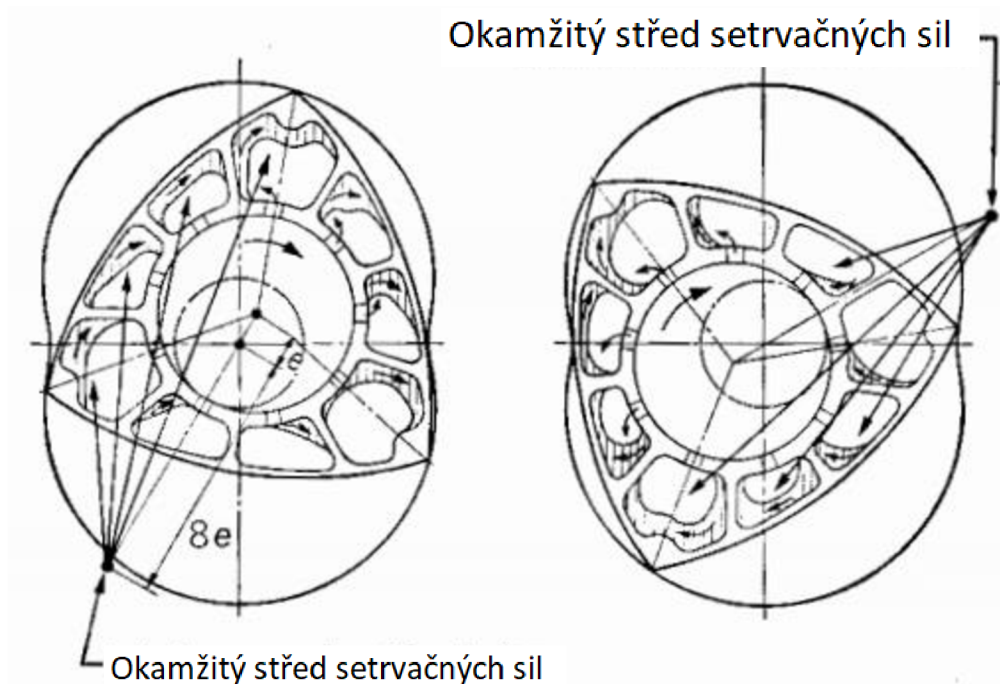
Chlazení rotoru směsí, prototyp Yamaha/Yanmar [13]
